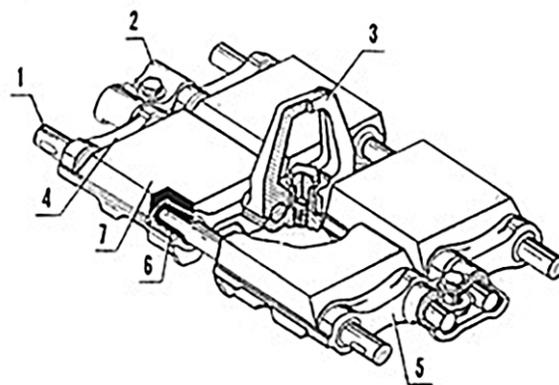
Звено гусеницы параллельного резино-металлического шарнира: 1 — палец; 2 — скоба; 3 — гребень; 4, 5 — звенья трака; 6 — резиновая втулка; 7 — резиновая подушка
